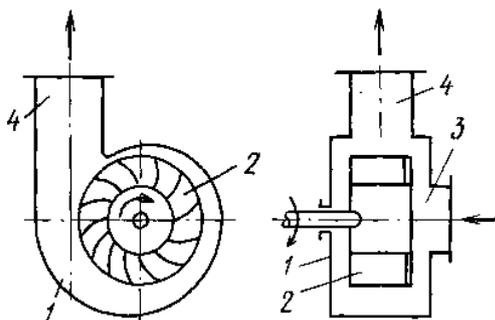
Схема центробежного компрессора: 1 – корпус; 2 – рабочее колесо; 3 – всасывающий патрубок; 4 – нагнетательный патрубок
